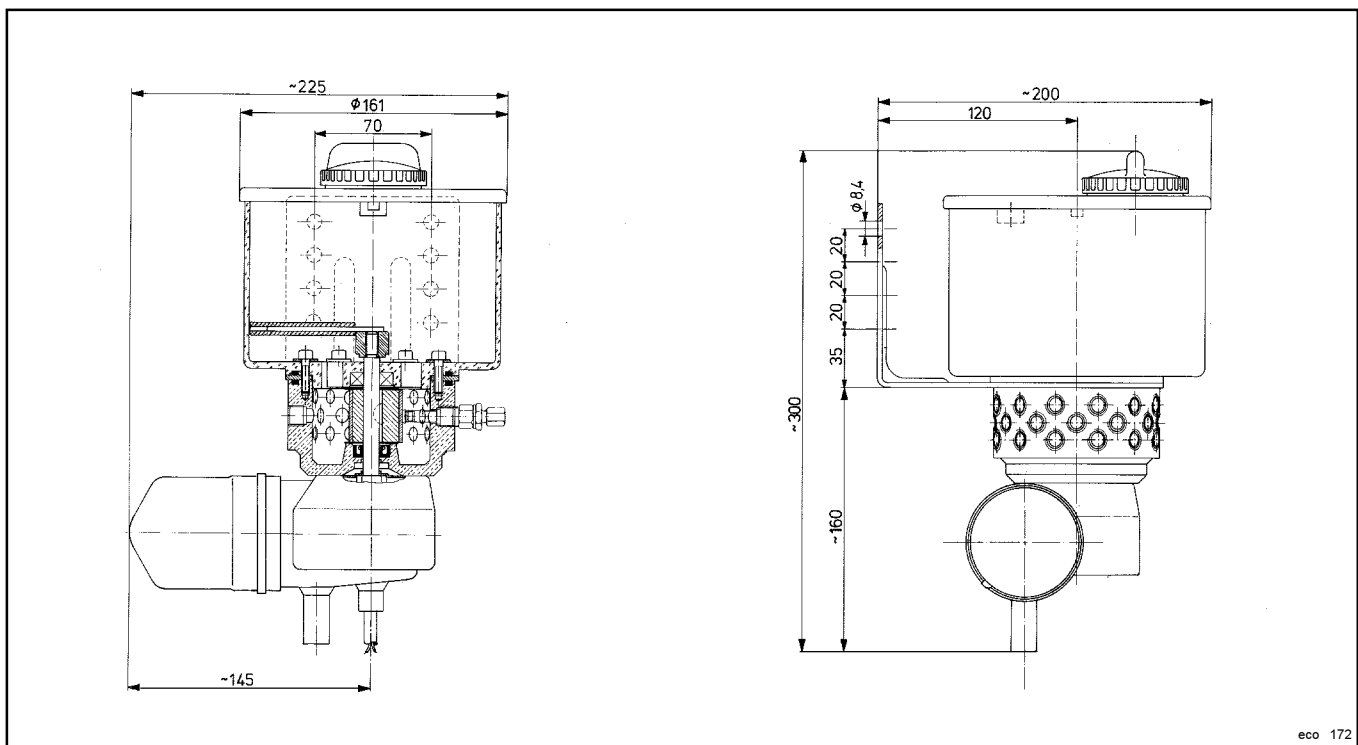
Pumpe ohne integrierte Steuerplatine
